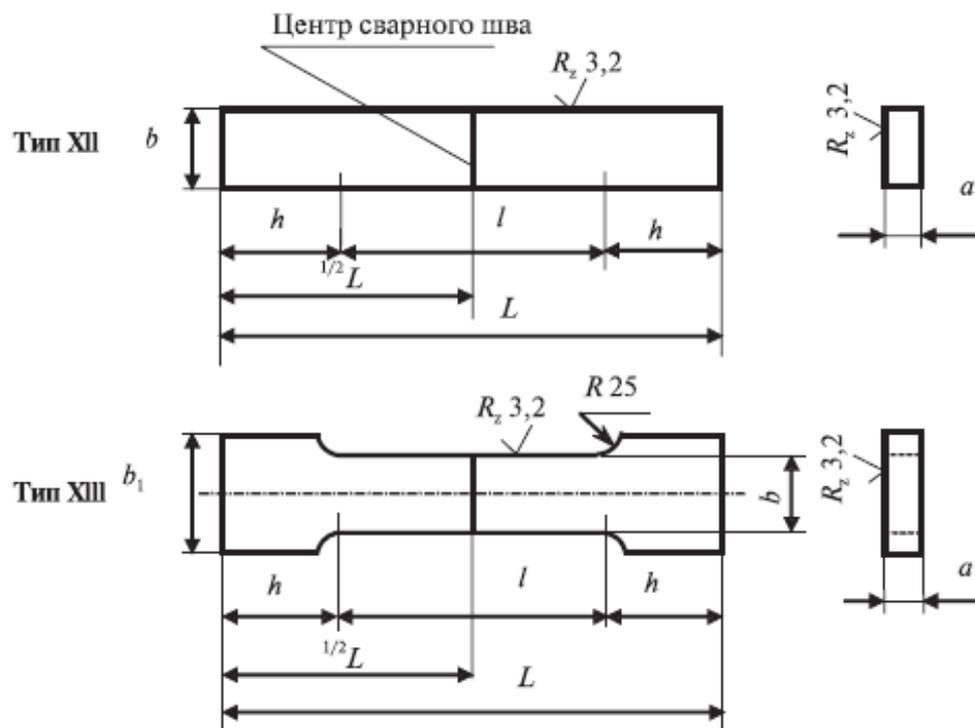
Форма и размеры образцов (типы XII и XIII) для испытаний сварного соединения на статическое растяжение
